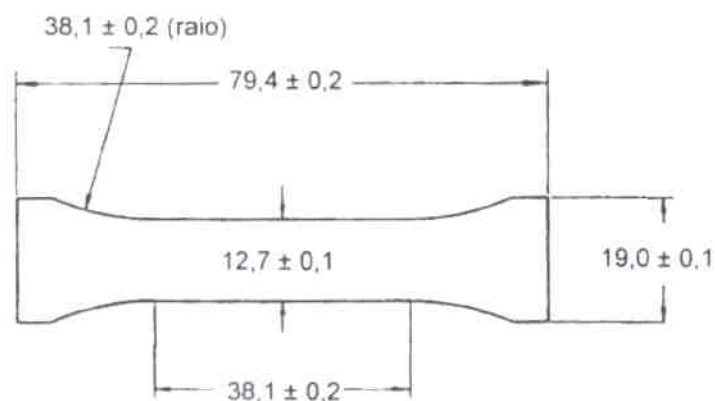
Dimensões do corpo-de-prova para espessura de parede inferior a 3,2 mm ou DN  $\leq$  200
